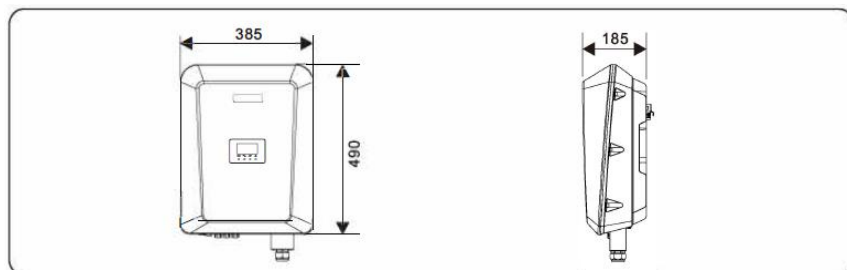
Dimensiones del inversor en vista frontal y lateral (unidad: mm)
